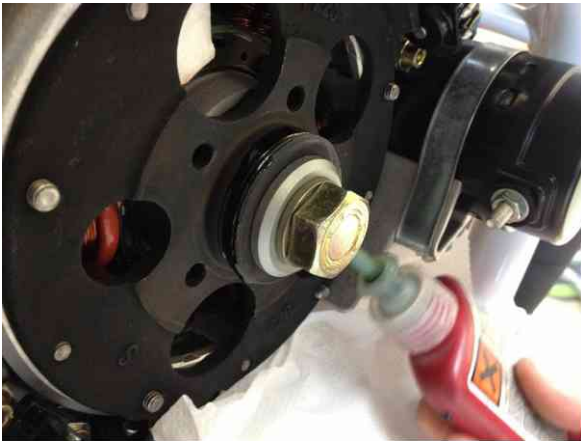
Loctite 648 auf Innen- und Außengewinde
